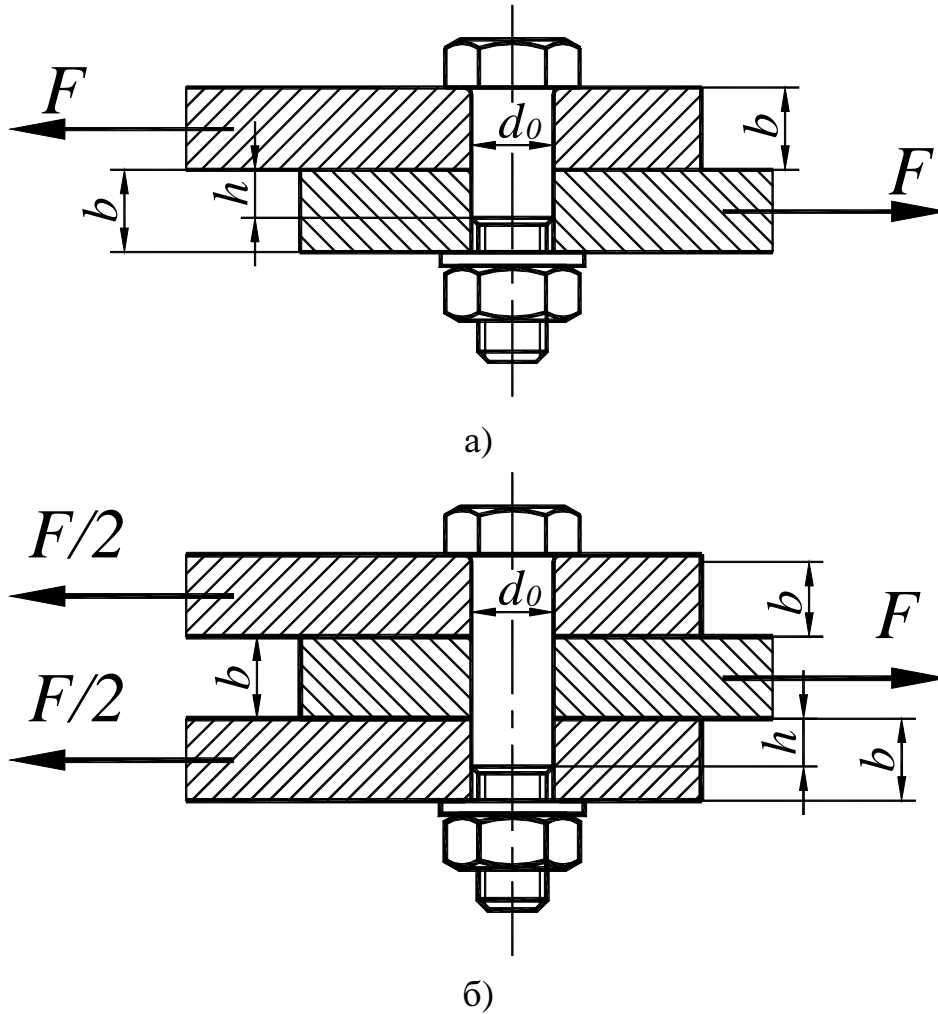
Розрахункова схема болтового з'єднання без зазору
